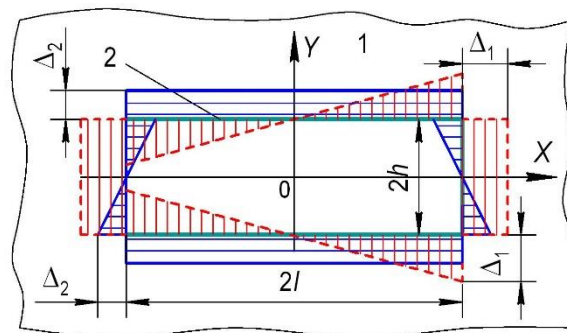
Схема сварного шва: 1 – пластина, 2 – сварной шов
